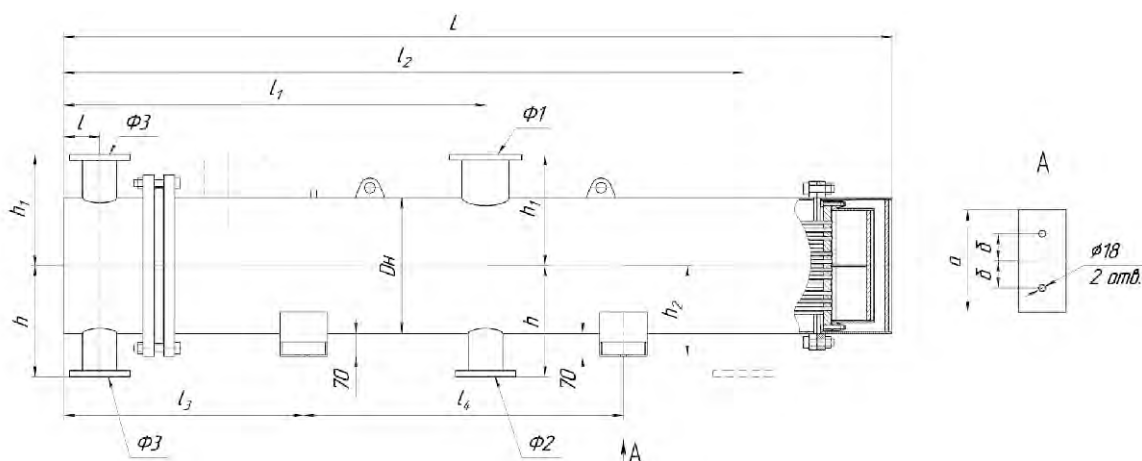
Габаритные и присоединительные размеры подогревателей MBH.
